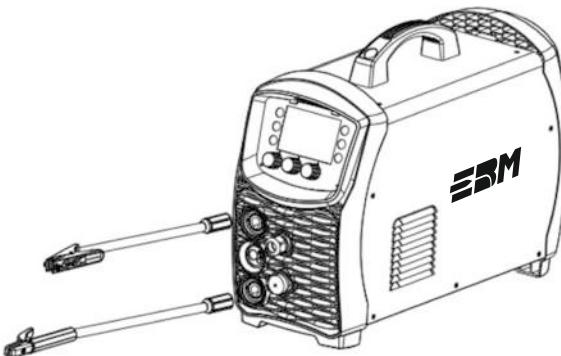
Схема подключения кабелей для MMA сварки
